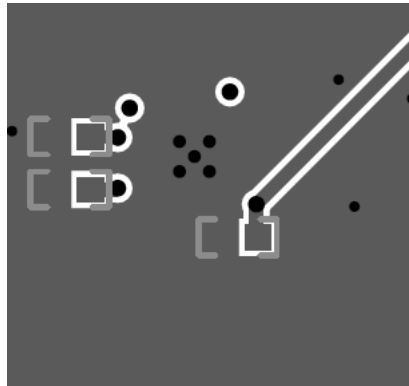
LMK3H0102 的 PCB 布局示例，底层
